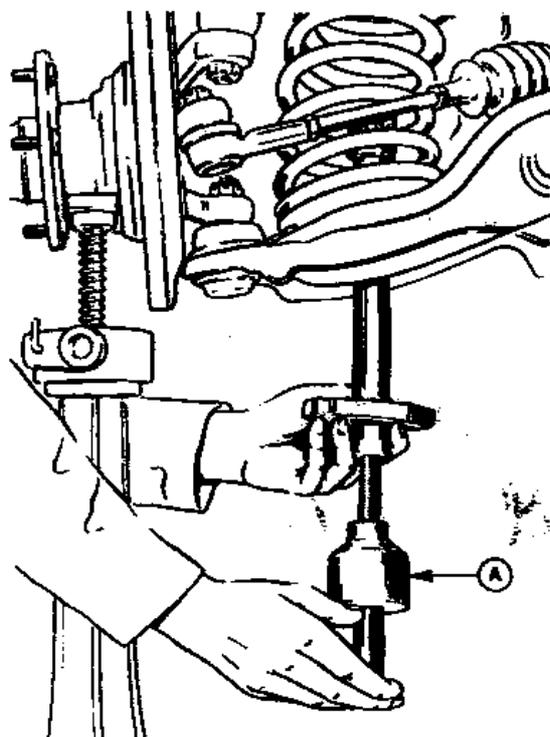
Установка съемника пружин подвески "А" (Разд.6)
